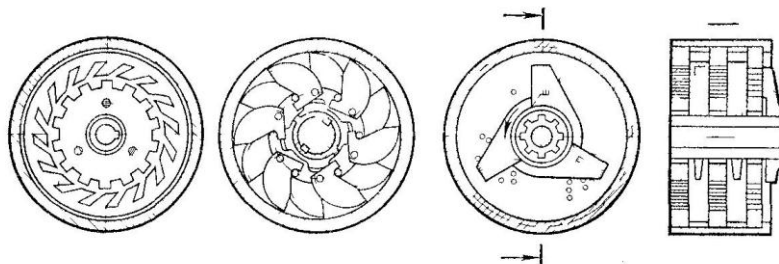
Схеми подрібнювачів: а) роторного типу; б) та в) багатоножового; г) багатодискового.
